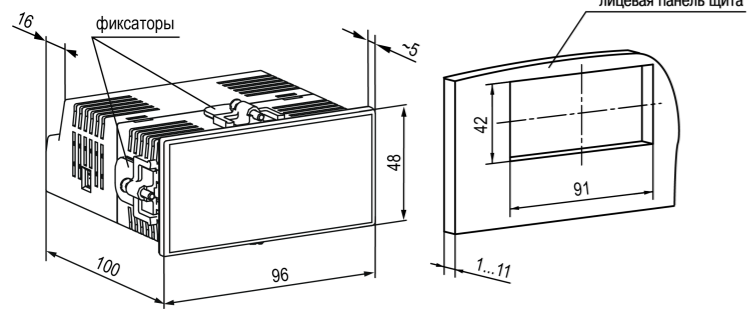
Габаритные размеры корпуса Щ2 и монтажного отверстия в щите
